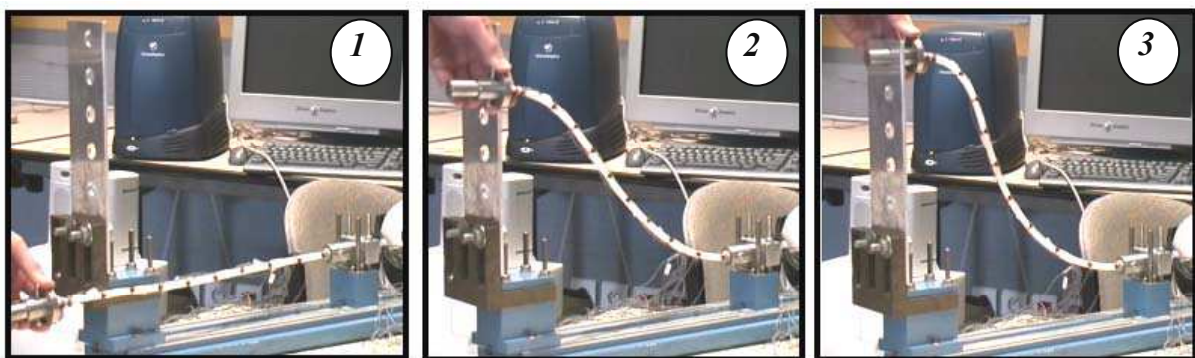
Quelques séquences d'une opération d'assemblage.
